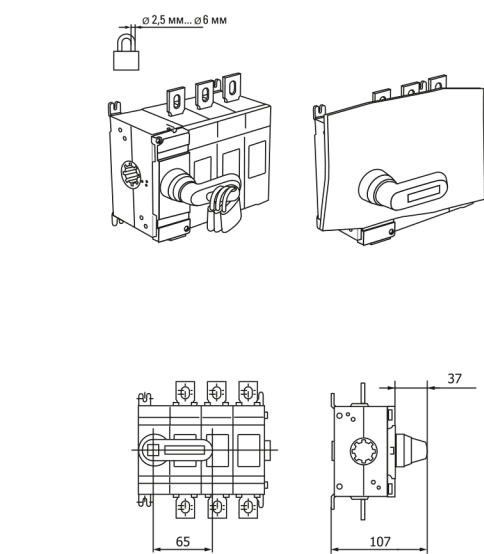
Установка рукоятки управления прямой установки 160-250А
